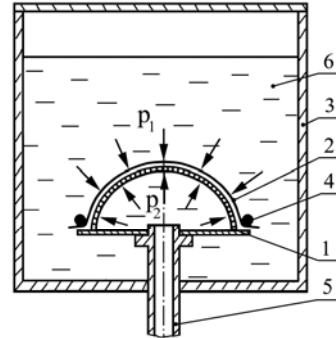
Схема корпусу камери для гідродинамічного формування:
